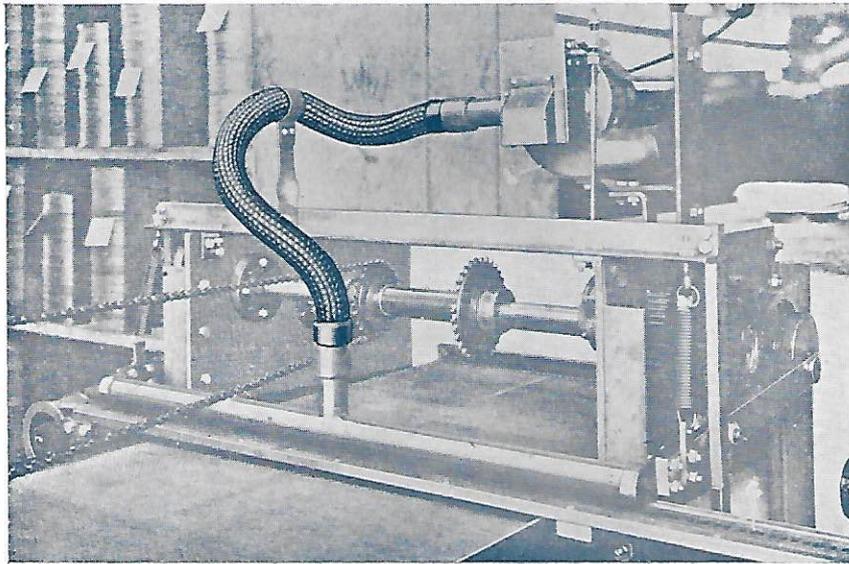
Transport pneumatique de pièces fragiles de bakélite au four à cuire.
